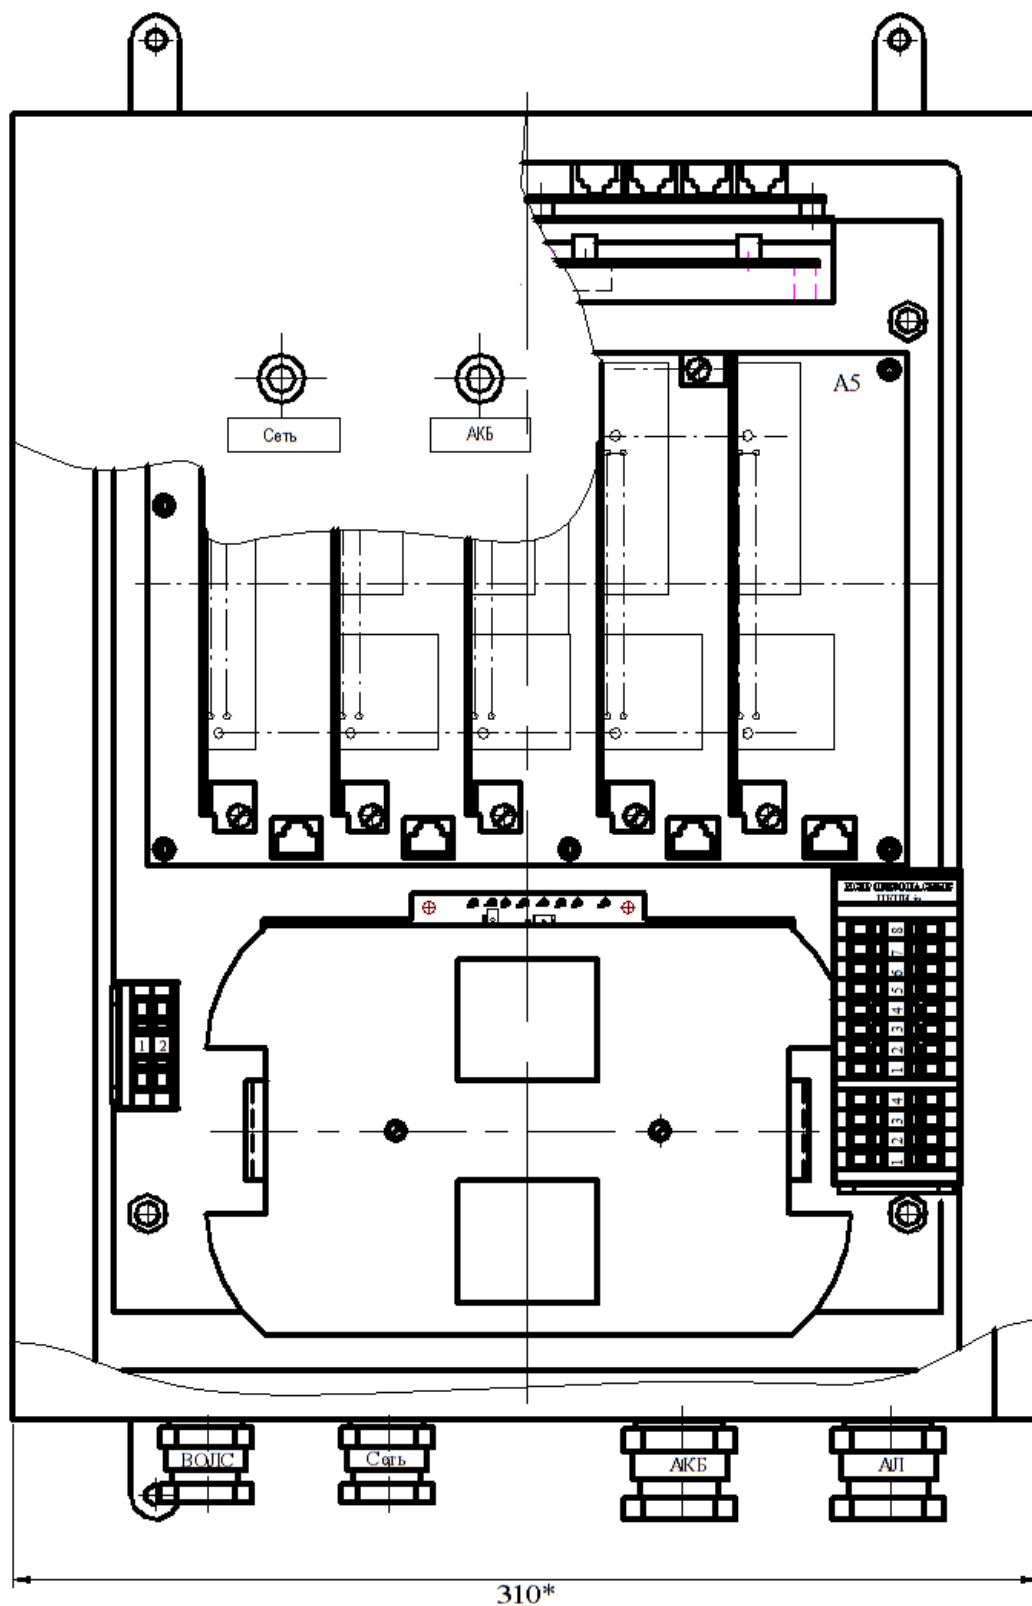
Чертёж корпуса IP- шлюза промышленного исполнения.
